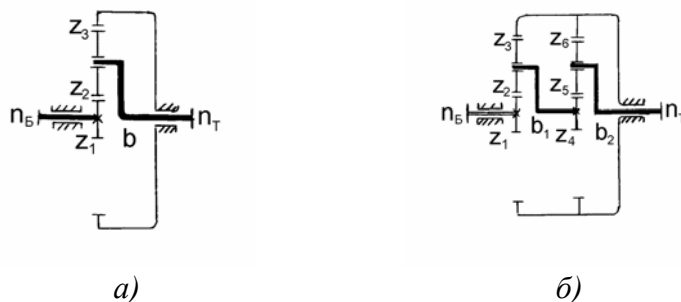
Схемы однорядных планетарных редукторов: а - одноступенчатый; б - двухступенчатый
